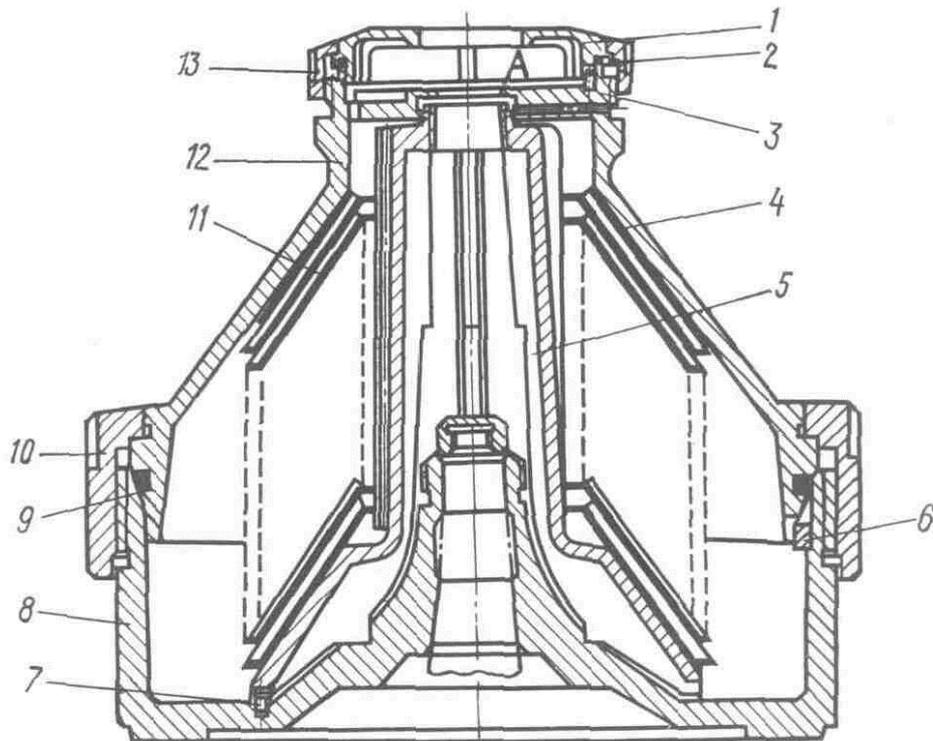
Барабан сепаратора ОМА-3М: 1 – крышка; 2, 9 – уплотнительные кольца; 3, 7 – штифты; 4 – верхняя тарелка; 5 – тарелкодержатель; 6 – шпонка; 8 – основание; 10 – большая затяжная гайка; 11 – рабочая тарелка; 12 – крышка барабана; 13 – гайка
